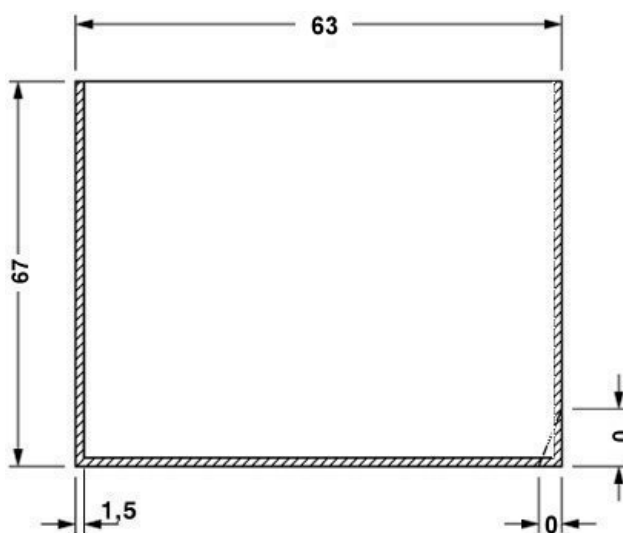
Dimensioned drawing 3 - valid for PCB 1; 2; 3; 4; 5 and 6, see Explosion drawing.
